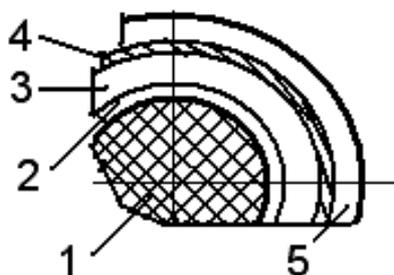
Схематический разрез формного цилиндра глубокой печати
